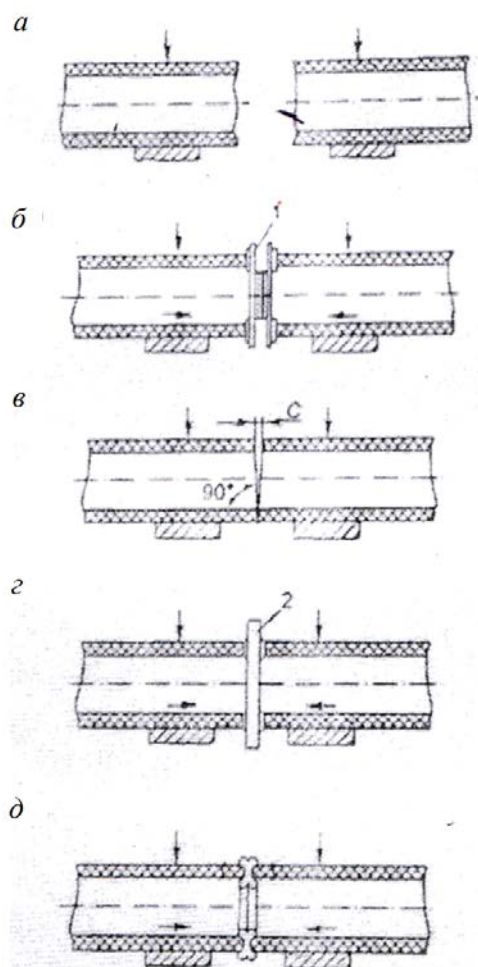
Последовательность процесса сборки и сварки встык труб из полиэтилена:
